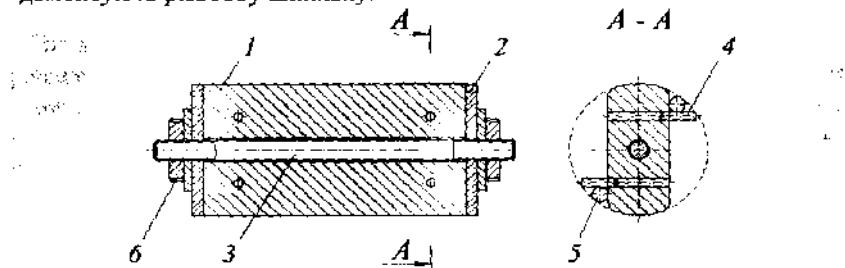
Технологічне пристосування для виготовлення каркасу секцій шарнірного валу: 1 – основа; 2 - торцева шайба; 3 – різьбова шпилька; 4 – фіксуючий палець; 5 – стержень; 6 – гайка
